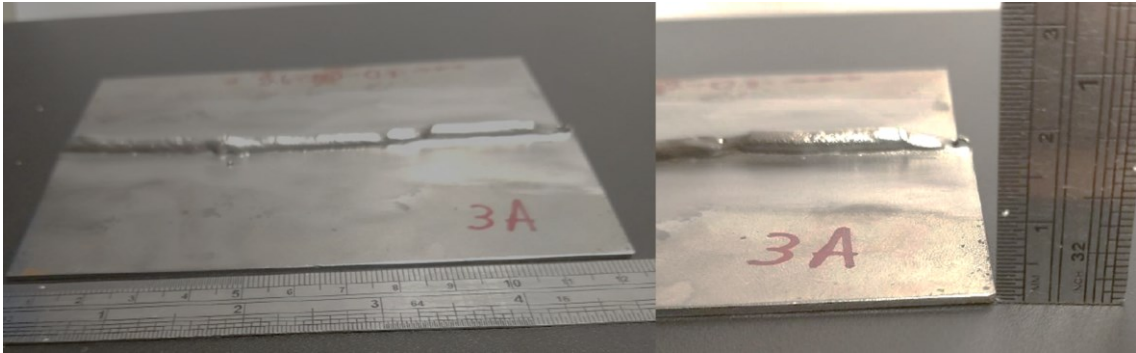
Cordão executado com passe "a ré", condição de soldagem 2 com empenamento mínimo. (Próprio autor)
